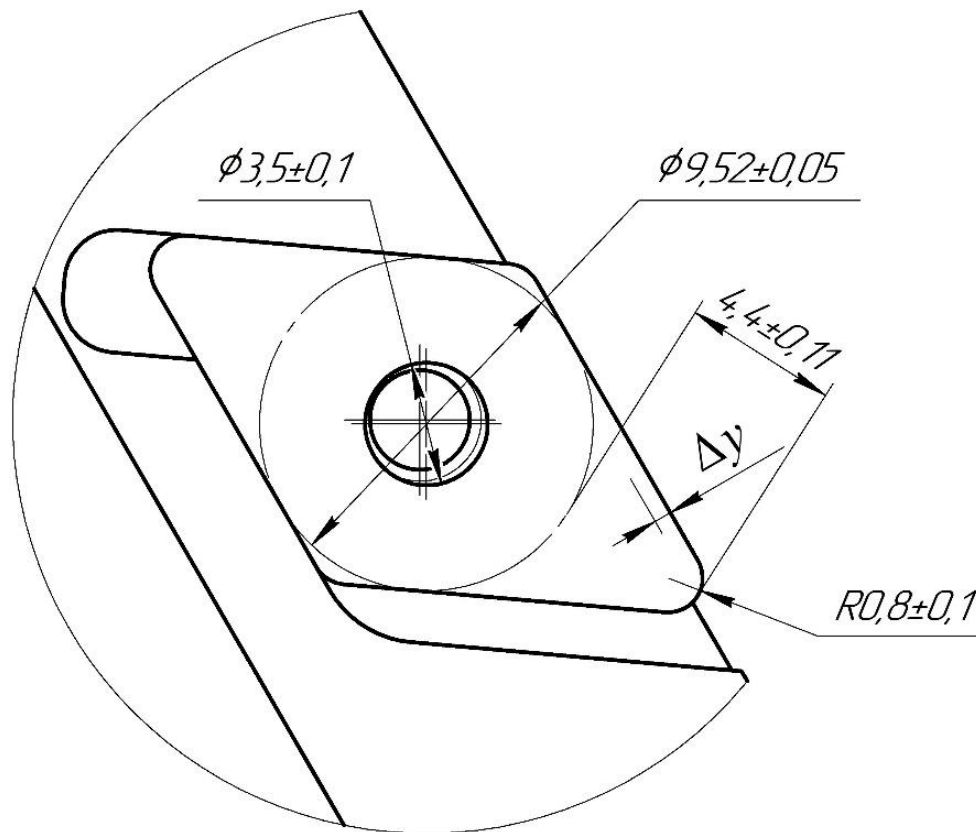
Схема розрахунку похибки базування пластини в кутовий паз
